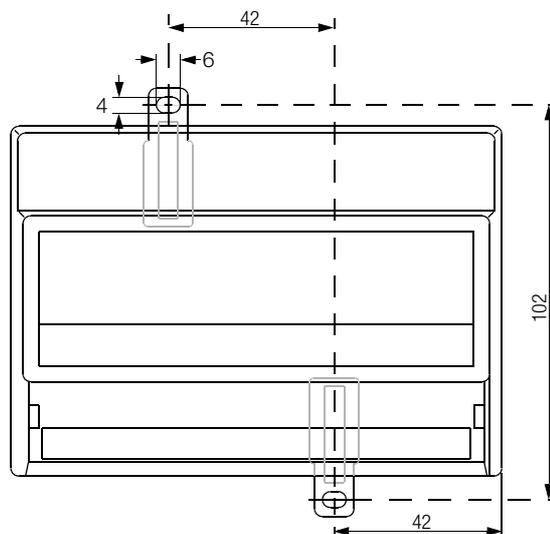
Maßzeichnung für Wandmontage (Frontansicht)
